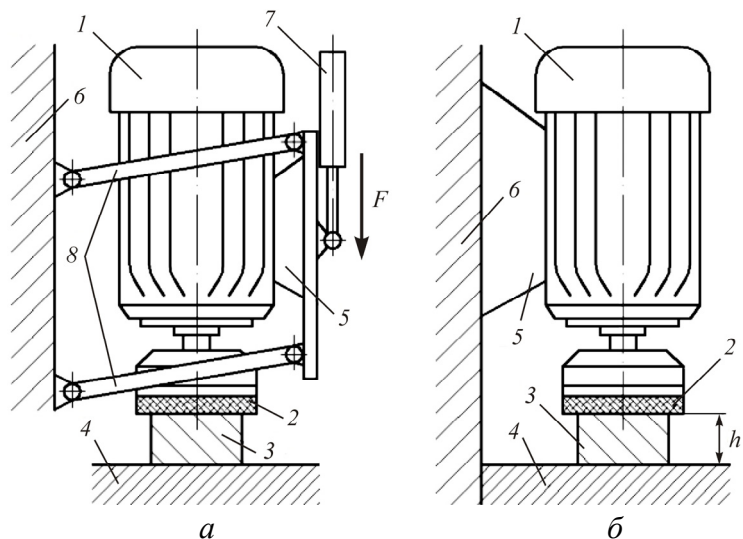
Принципиальные схемы шлифования торцом круга: 1 – шлифовальный электродвигатель; 2 – шлифовальный круг; 3 – обрабатываемая деталь; 4 – базовая поверхность; 5 – подмоторная плита; 6 – станина; 7 – пневмоцилиндр; 8 – параллелограммный механизм
